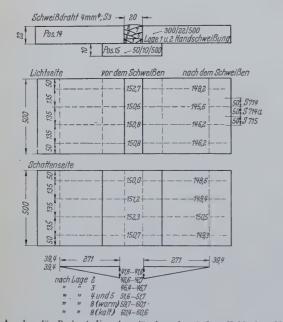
Angaben für Probe 4. Unterlagsplättchen ohne äußere Kehlnähte. Masse, Lage der Schweißungen, Schweißdaten und Schrumpfung. Ausschneiden der Proben für Ermüdungsversuche.
